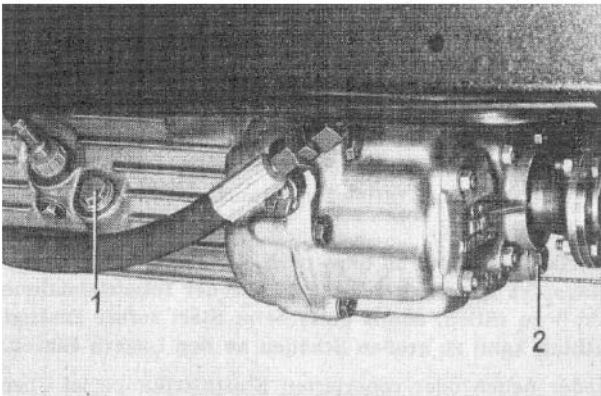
Ölkontrolle, Wechselgetriebe mit angeflanschem Kriechganggetriebe
